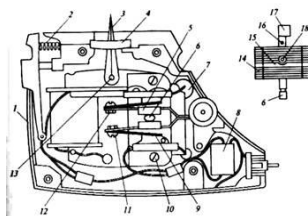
Электробритва «Чайка-304-авто» (монтажный корпус): 1 – монтажный корпус; 2 – пружина; 3 – поводок кулисы; 4 – уплотнитель;
